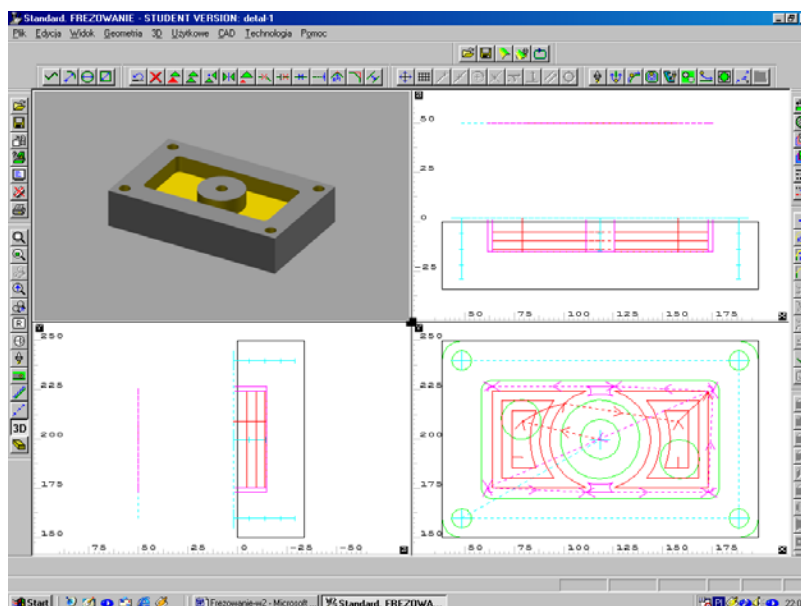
Ustawienia parametrów obróbki wykańczającej kieszeni
